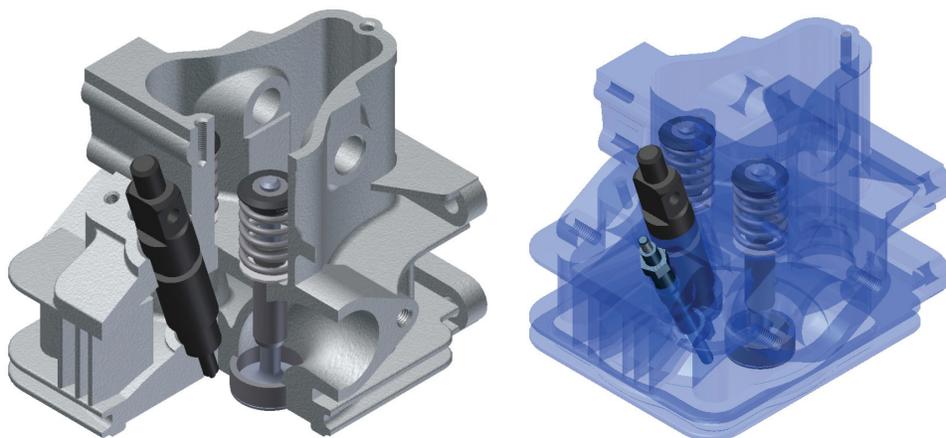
Трехмерная сборочная модель головки двигателя МД-8
